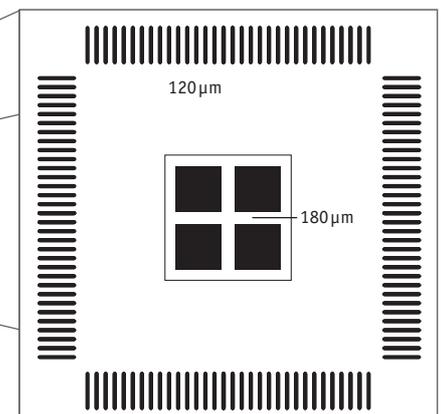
QFP-Bauelement mit heat sink Anschlüssen
